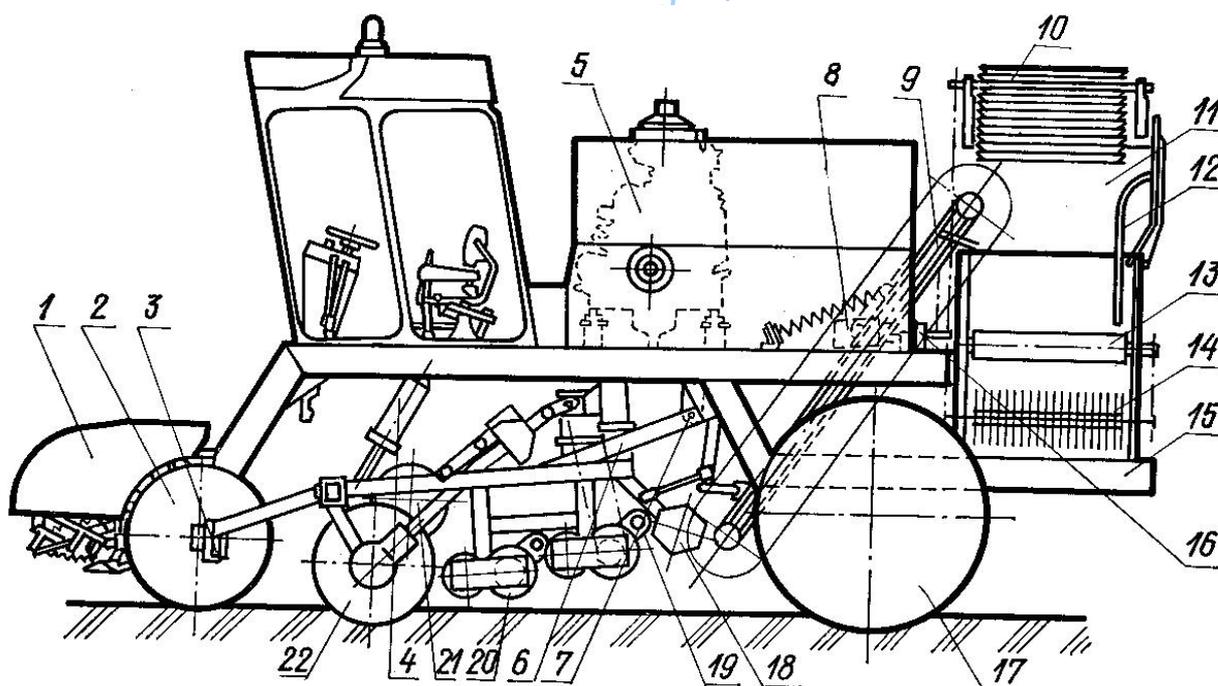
Конструктивная схема корнеуборочной машины КС-6
